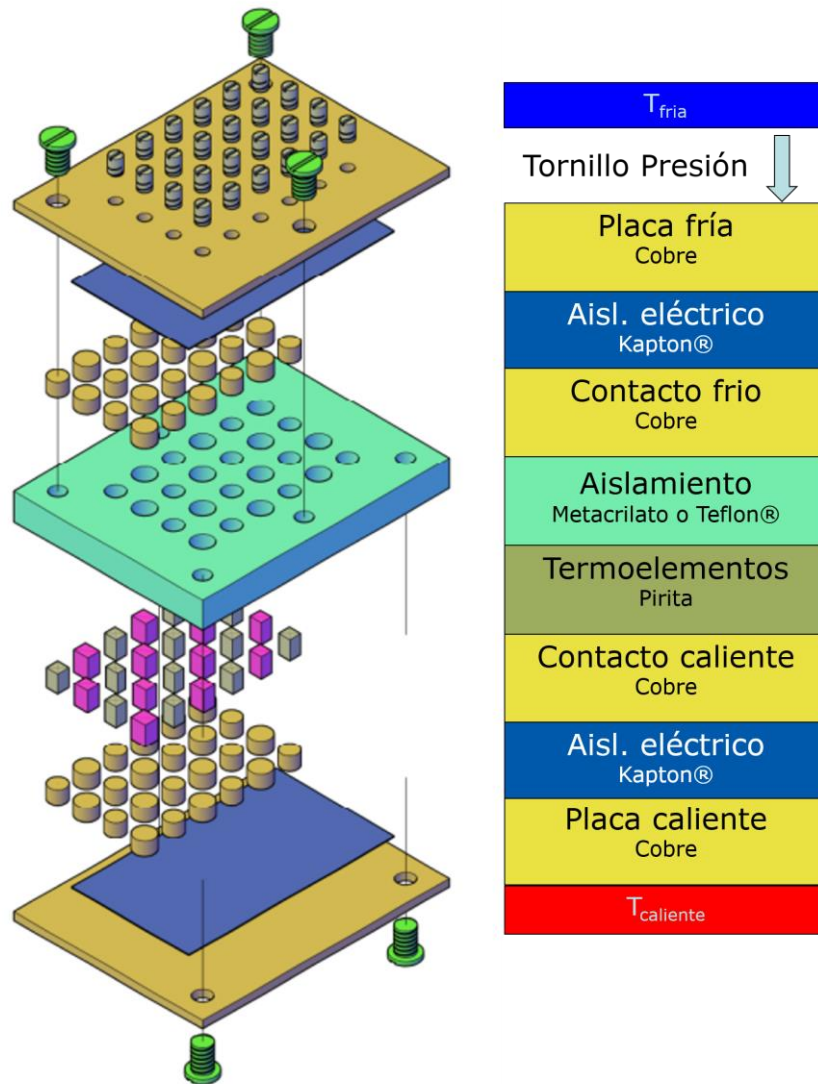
Esquema final del dispositivo ¹⁰.
